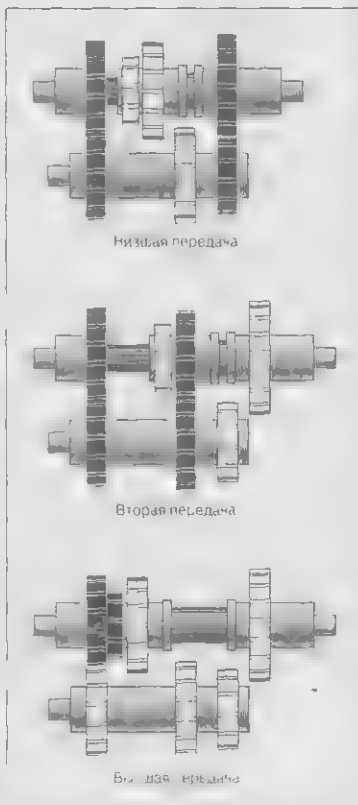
Шестерни трансмиссии коробки передач в разрезе
